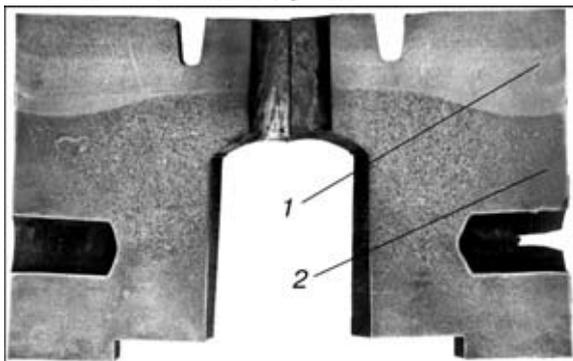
Макроструктура поперечного сечения штампа, наплавленного способом ЭШН стружкой инструментальной стали 5ХНМ: 1 — наплавленный металл; 2 — штамп
